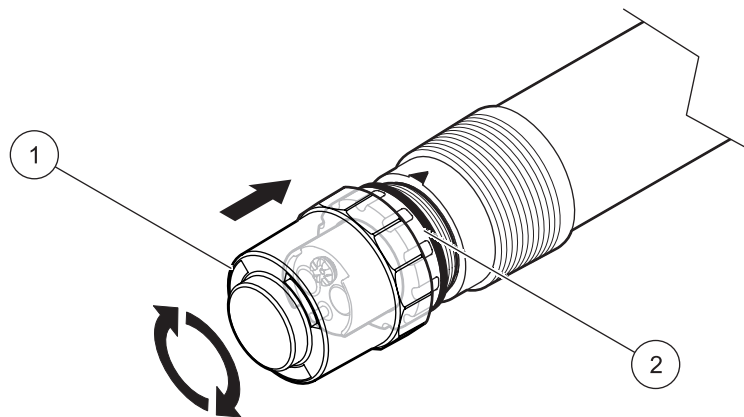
Deckel des Aufbewahrungsbehälters als Werkzeug/Aufschraubhilfe für den Schraubring
